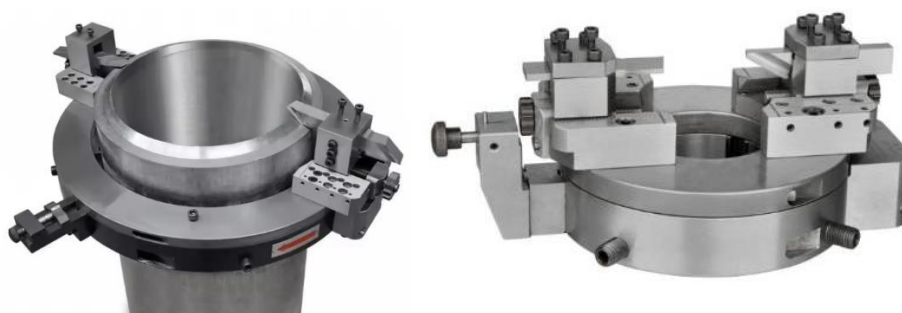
Труборезы для вырезки патрубков и подготовки кромок
